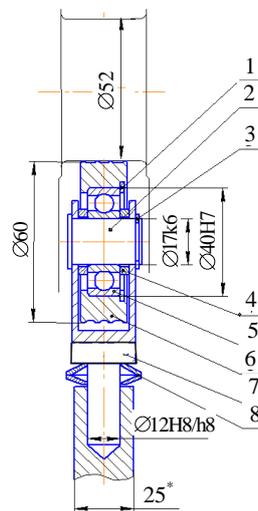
Ролик для ППД шеек коленчатого вала:
